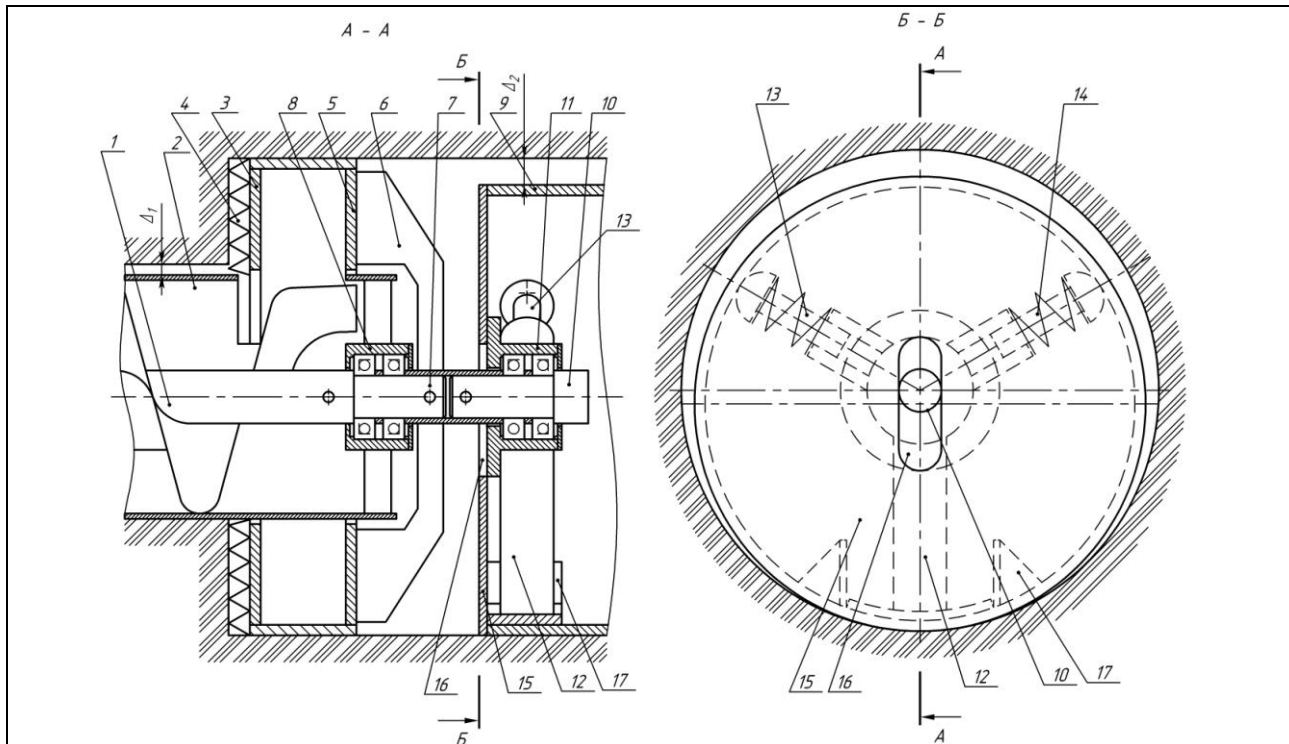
Расширитель обратного хода с якорно-прицепным устройством. 1 – секция шнекового бурового става; 2 – приемный лоток; 3 – барабан; 4 – режущие ножи; 5 – задняя стенка; 6 – крестовина; 7 – вал; 8 – подшипниковая опора; 9 – труба-кожух; 10 – якорно-прицепной механизм в виде вращающейся оси; 11 – подшипниковая опора; 12, 13, 14 – радиальные лучи; 15 – стенка заглушка; 16 – радиальный паз; 17 – ограничитель.
